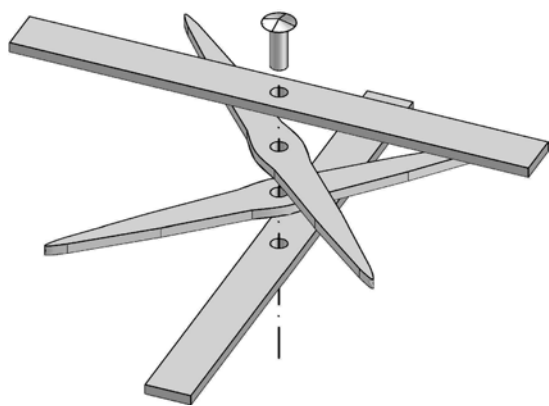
Konstruktionsschema Fenstergitter Typ IIB2.
